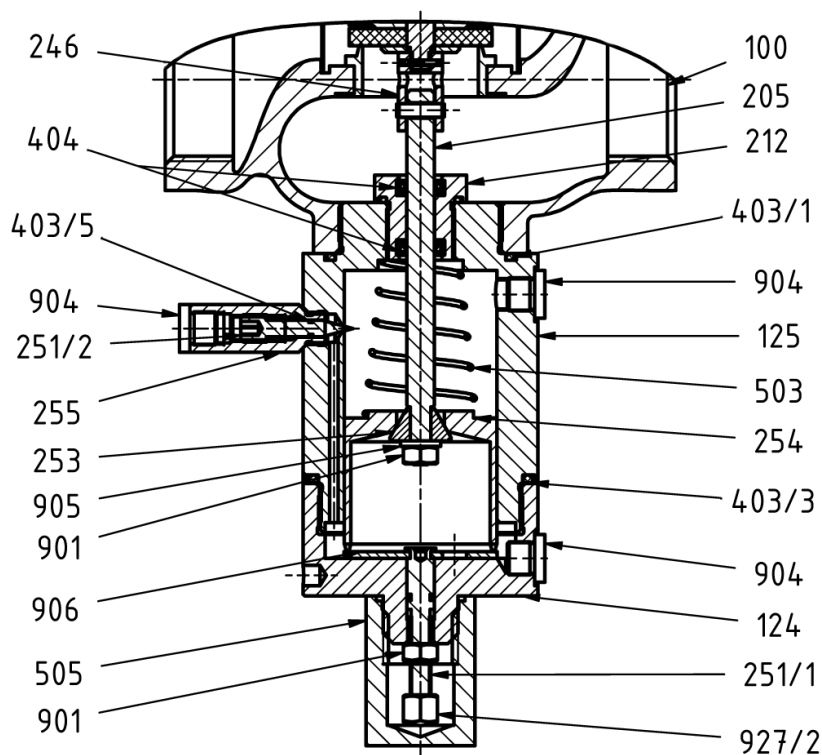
Ausführung für Gewindeventil G 1 1/2 / *Fig. 3 version for threaded valve G 1 1/2
